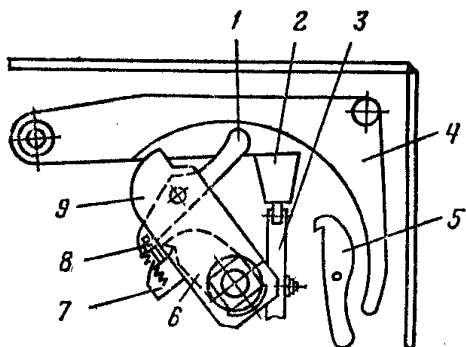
Регулировка включающего и удерживающего механизмов привода ПП-67:
